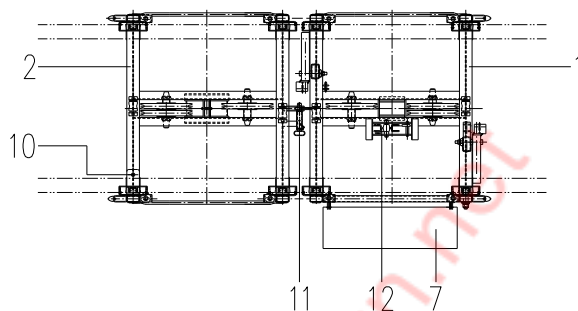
安装牵引小车 Fig. 4-25 Fitting the jib trolleys
